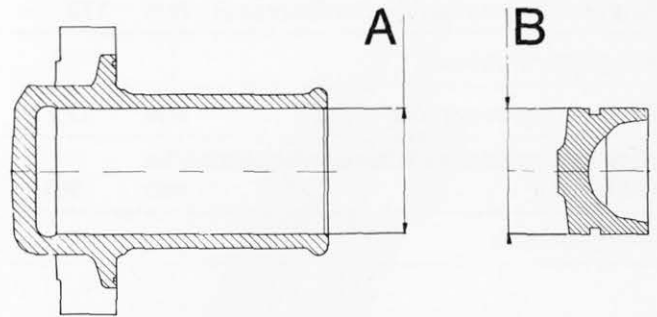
Kolben- und Hubzylinderdurchmesser.
